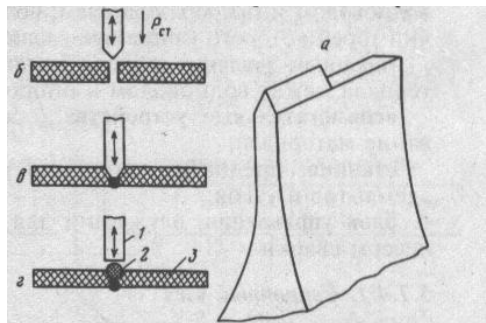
Форма волновода (а), применяемого для V – образной разделки свариваемых кромок (б) с одновременным проплавлением корня шва (β) и последующей сваркой (з): 1 - волновод-нож; 2 – пластмассовый присадочный пруток; 3 – свариваемые детали
